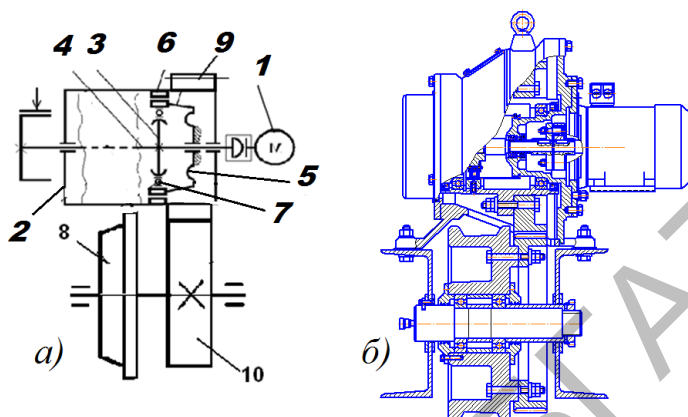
Механизм передвижения : а – схема; б- конструкция
